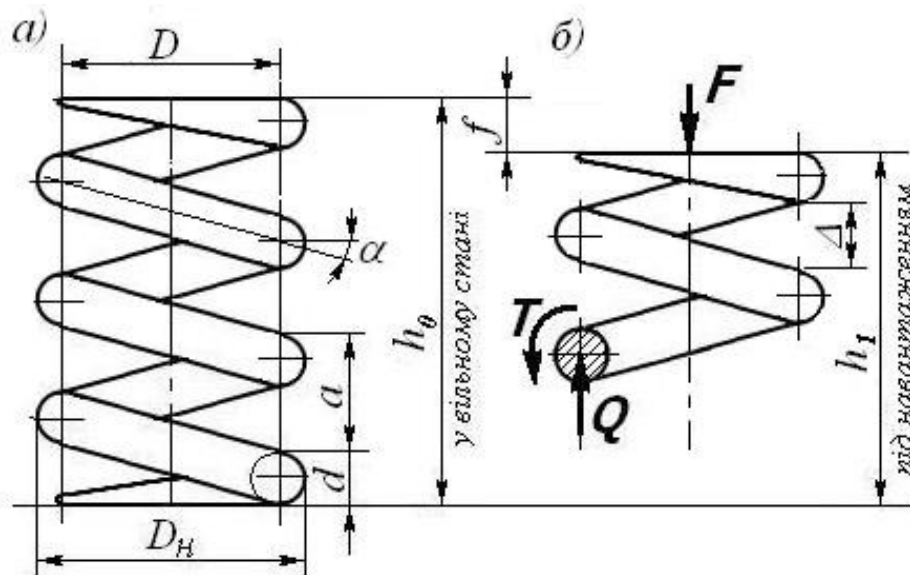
Розрахункова схема циліндричної гвинтової пружини
